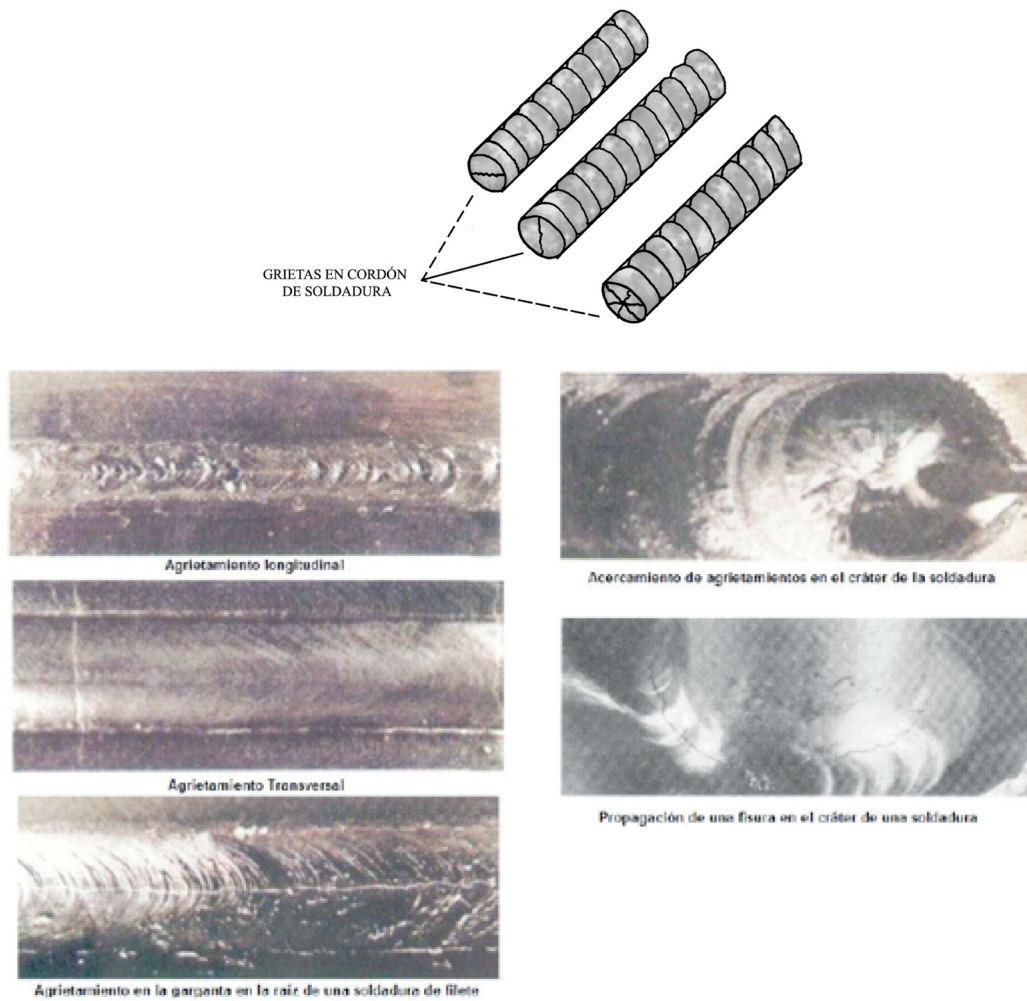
Defectos en la soldadura: agrietamiento
